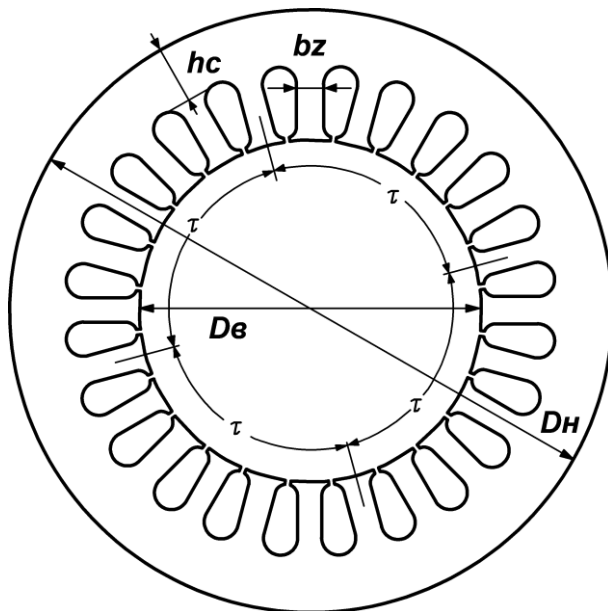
Пластина пакета статора с основными размерами и полюсными делениями,
